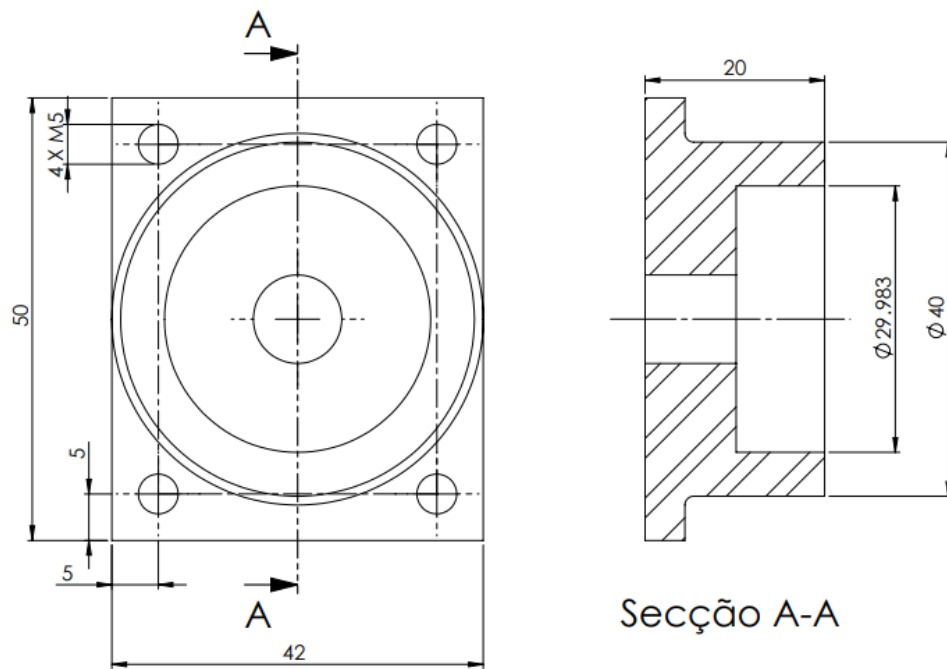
Desenho técnico da caixa de montagem do rolamento.
